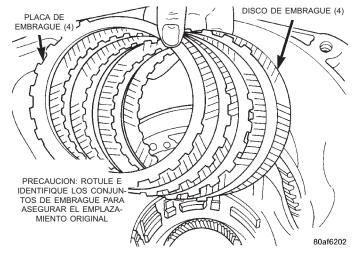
Desmontaje del conjunto de embrague de 2/4
